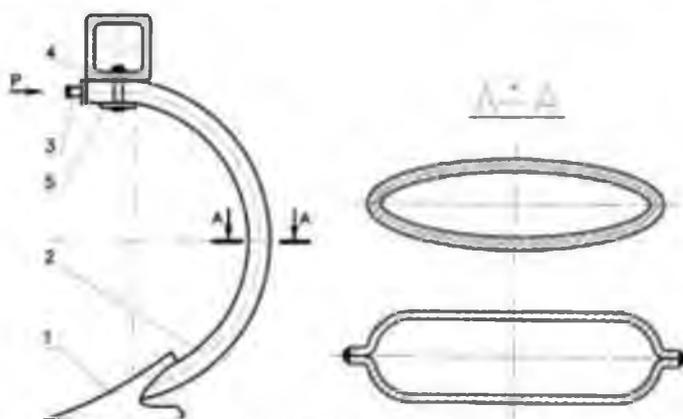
Принципова схема віброімпульсного робочого органу
